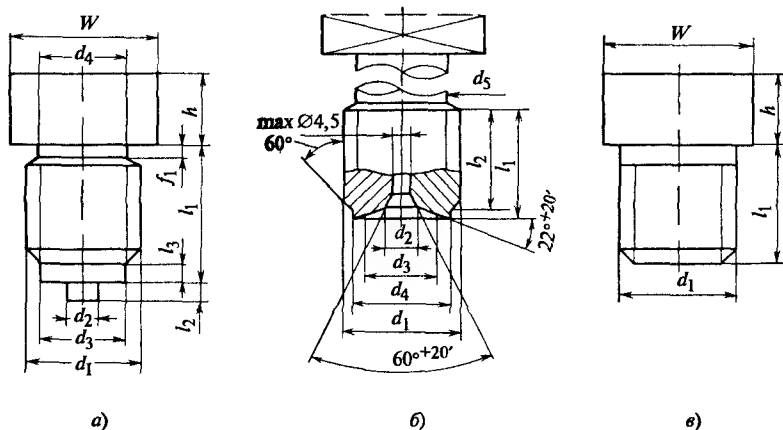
Варианты изготовления присоединительного штуцера по EN 837-1 и EN 837-3:
